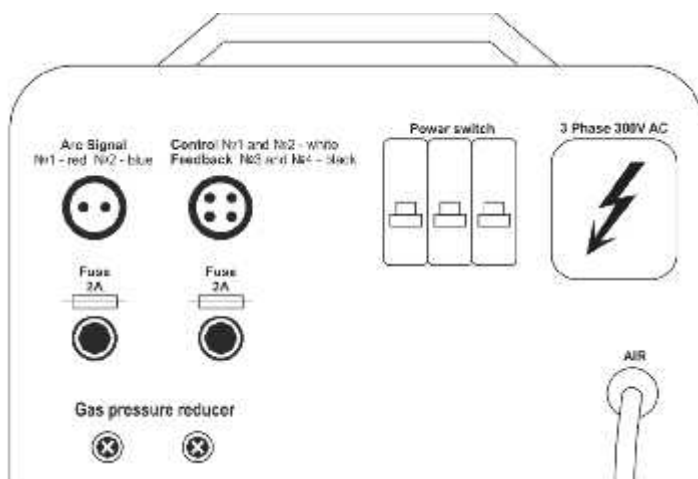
Задня панель WELDING DRAGON JS CUT-130
